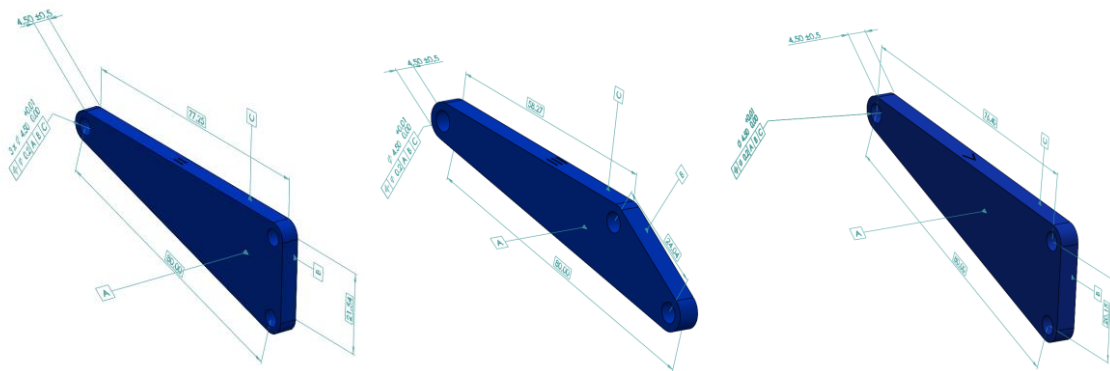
Tolerancias dimensionales “Barra 1” dedos
